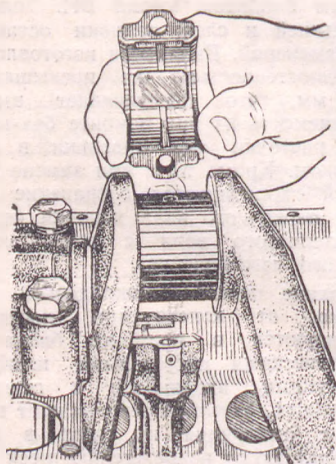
Проверка зазора в шатунном подшипнике при помощи контрольной пластинки.
